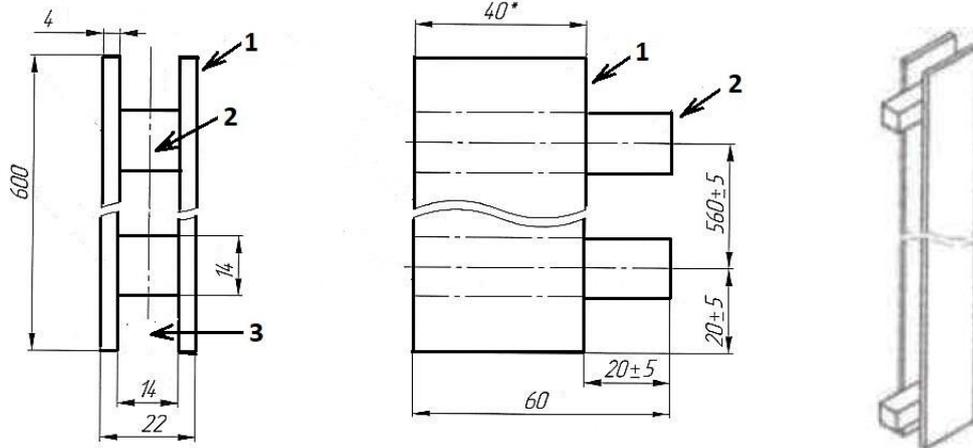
Конструкция и размеры кронштейнов ККП-60 с опорными сухарями одинаковой длины:
